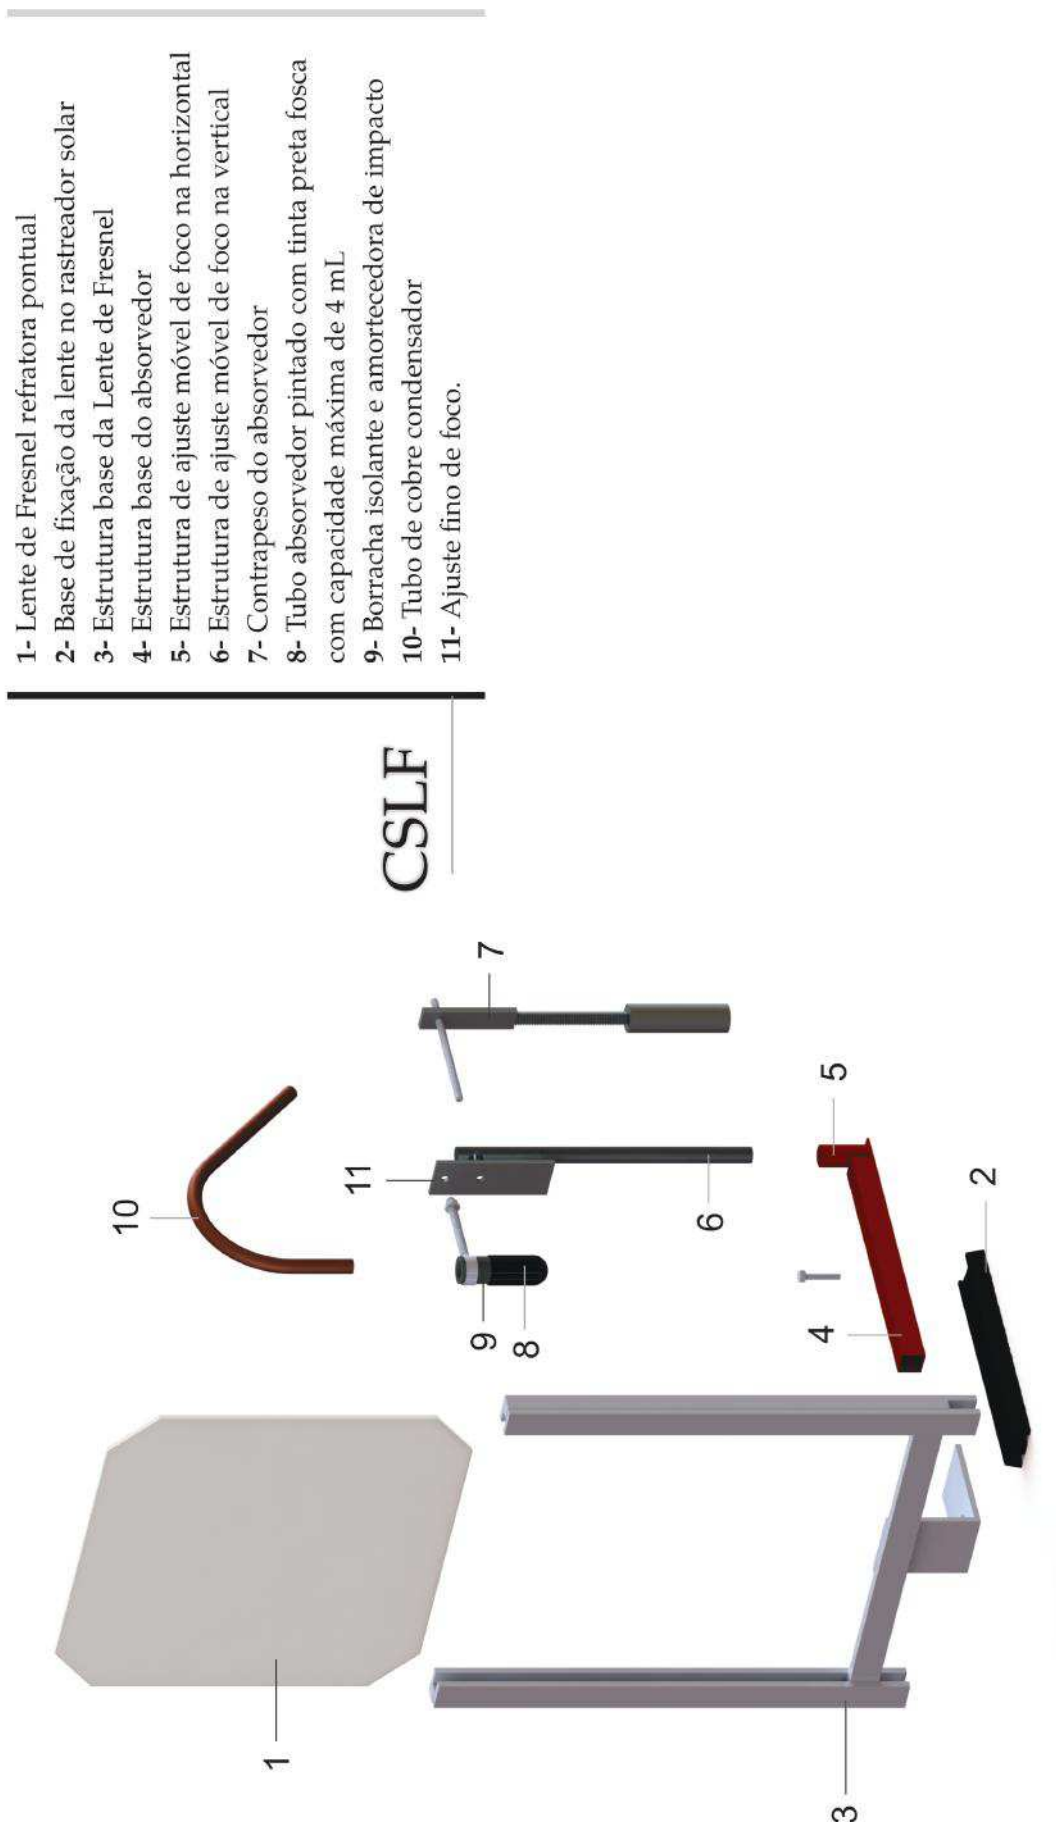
Vista explodida do Concentrador Solar de Lente de Fresnel.
